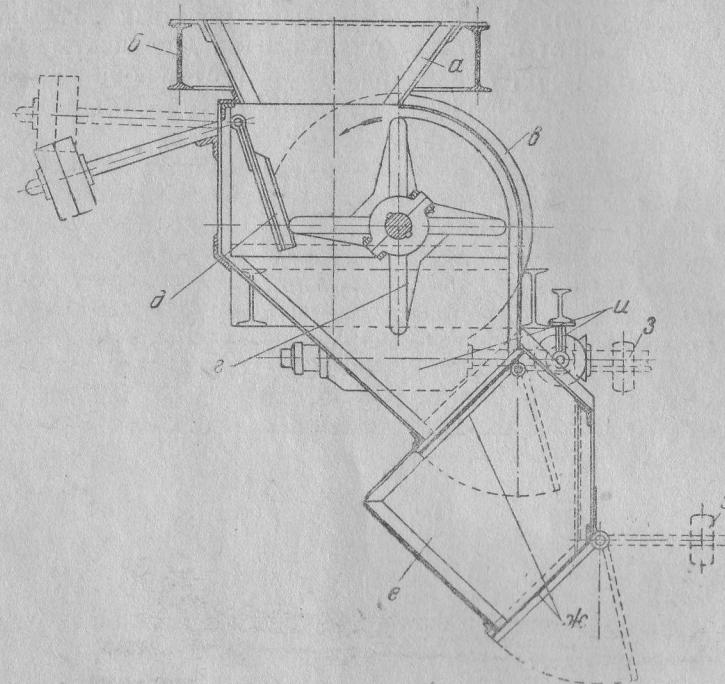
а—воронка; б—рама для укрепления воронки; в—турникетная рубашка; г—турникеты (звездочки); д—предохранительный щит с противовесом (для предотвращения поломки турникетного вала при заклинивании кусков выгружаемого материала); е—двухклапанная коробка; ж—клапаны; з—противовесы клапанов; и—механизм для приведения во вращение турникетного вала и для открытия клапанов (клапаны закрываются под действием противовеса).
